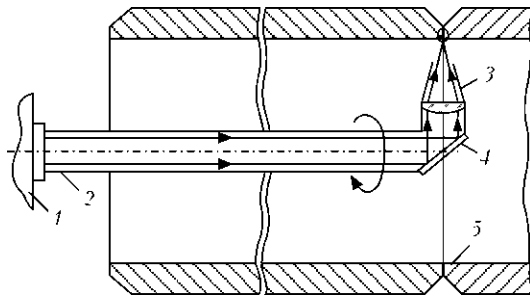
Схема орбитальной сварки корневого шва для монтажа трубных стыков: 1 — CO₂-лазер; 2 — поворотный лучепровод; 3 — лазерная сварочная головка; 4 — поворотное зеркало; 5 — неповоротный трубный стык
